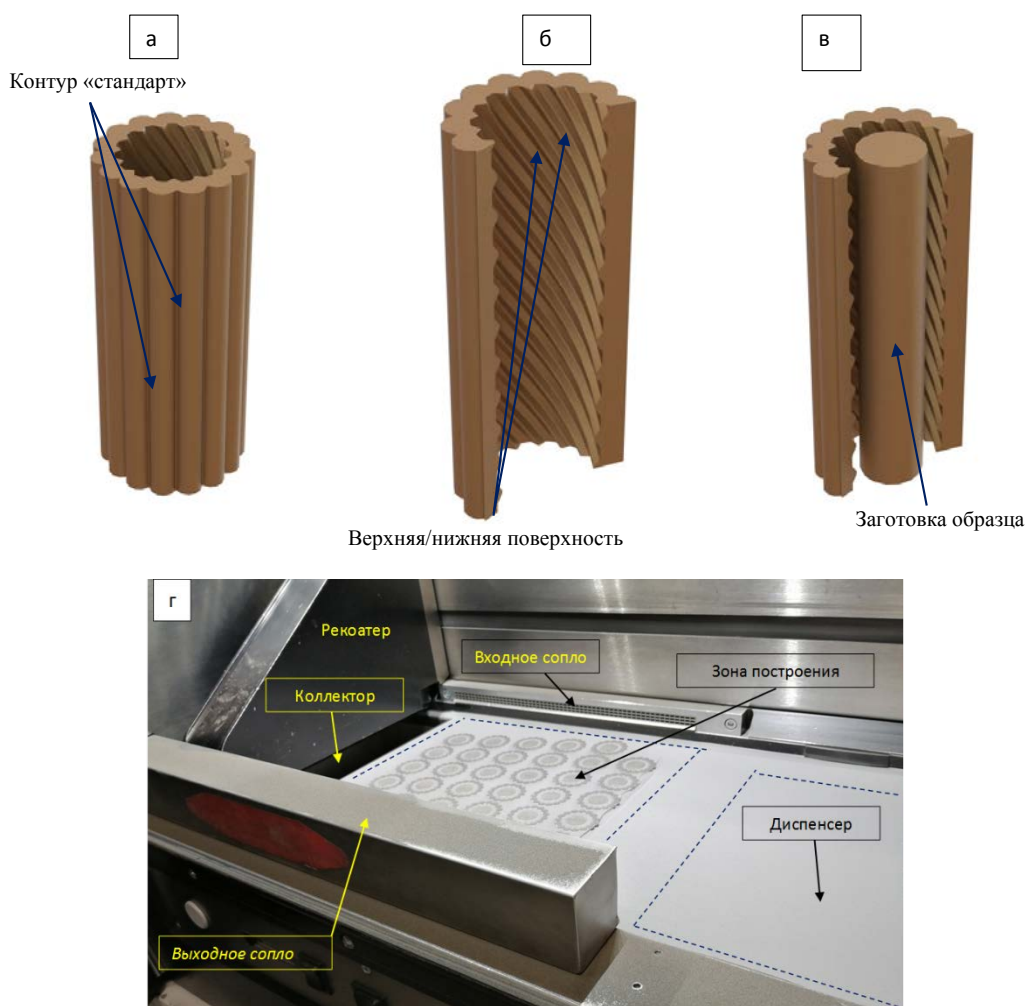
Рендеры контейнерного образца (а, б), заготовки для испытания механических свойств (в), камера построения после окончания процесса СЛС
